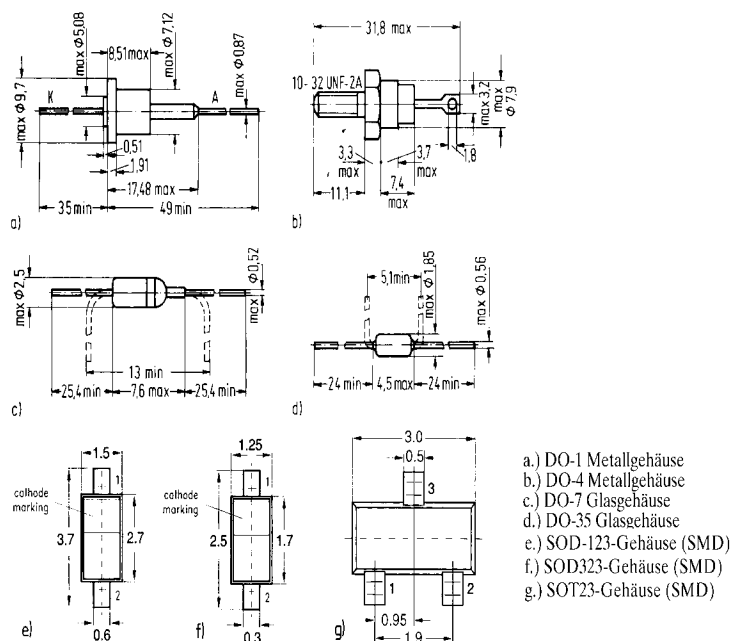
Beispiele einiger Gehäuseformen für Dioden.
